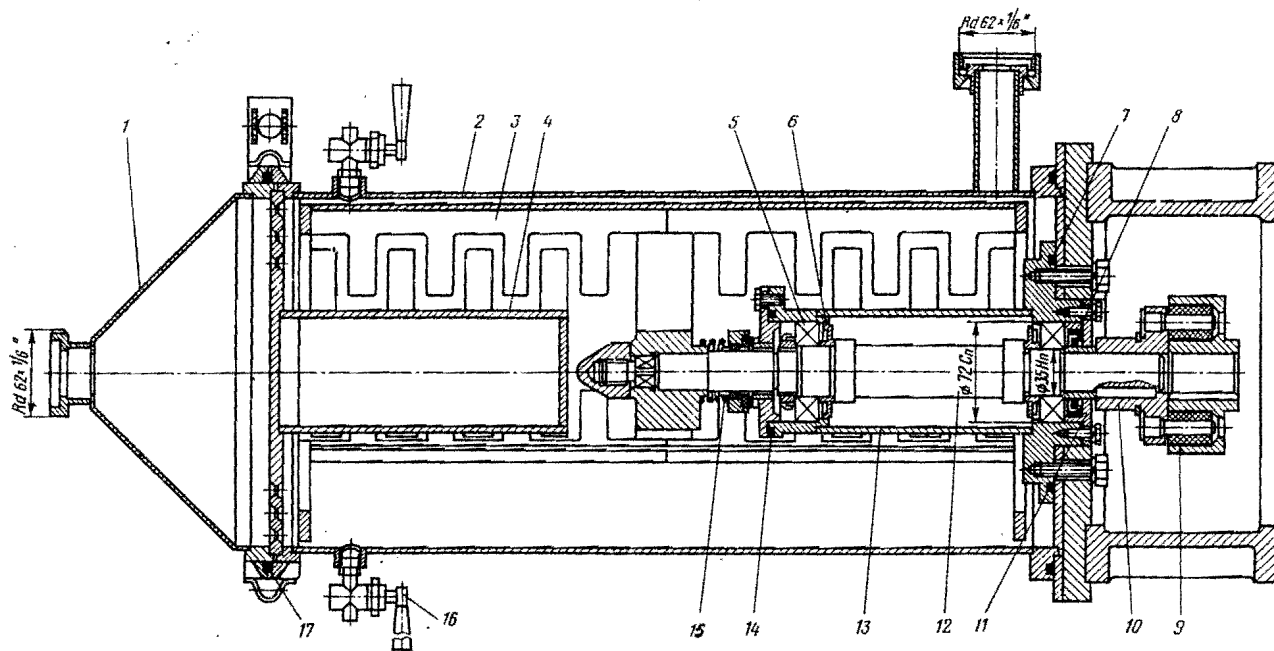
Общий вид маслообразотника маслообразователя марки РЗ-ОУА1:
